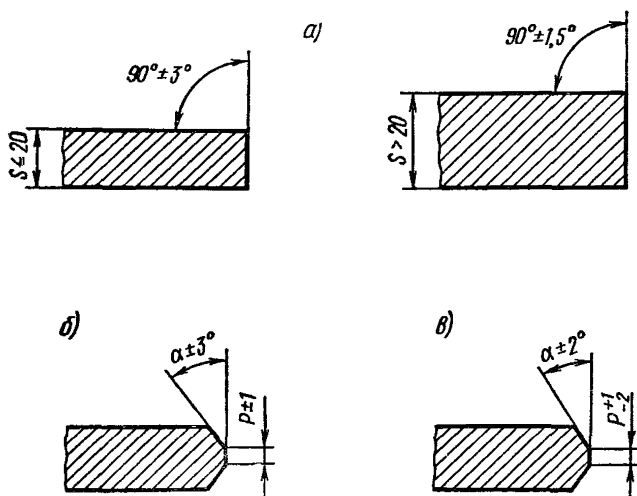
Допускаемые отклонения при подготовке кромок под сварку:
